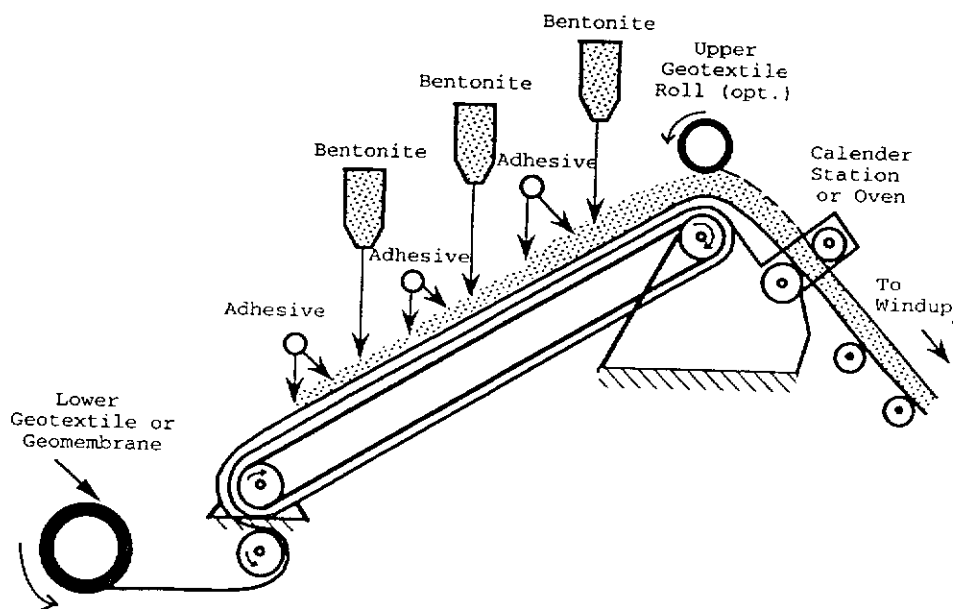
Tørr bentonitt bundet i en geotekstil som er laminert til en geomembran
